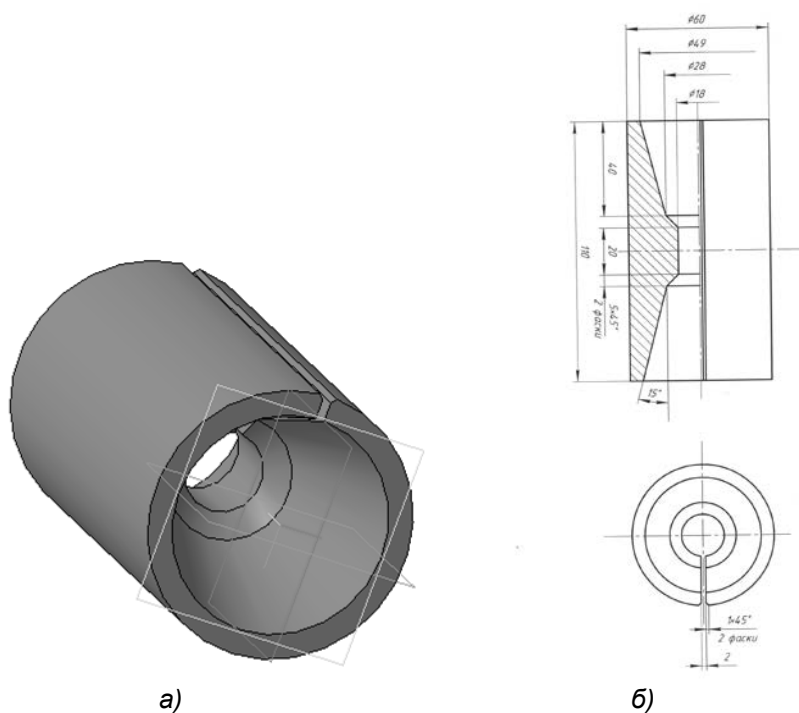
Конструкция цилиндрического концентратора: 3D-модель (а); эскиз (б)
